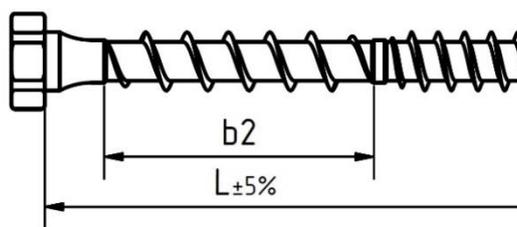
Schmid Schrauben RAPID® T-Con mit Gewinde am Schaft
